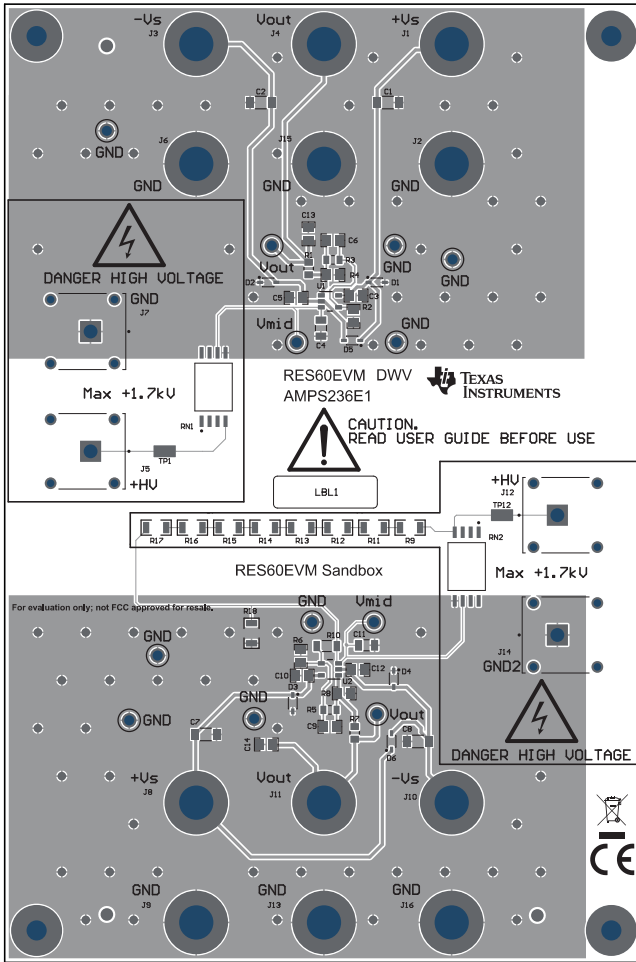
RES60EVM PCB 布局复合视图 (顶视图)
